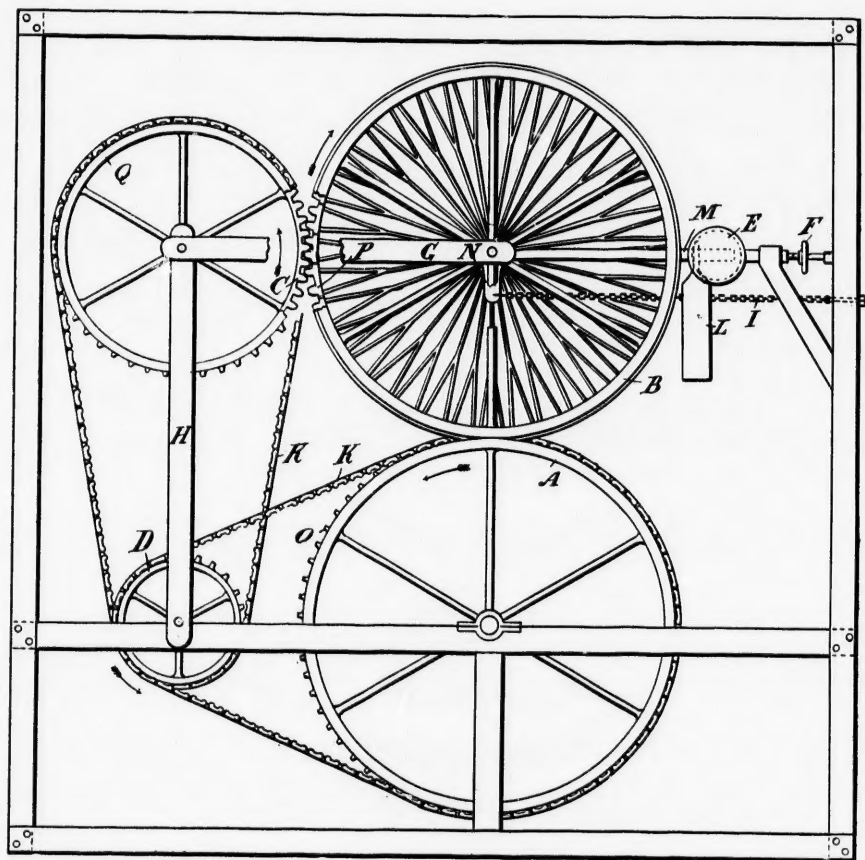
Élévation, ou vue de front, du Moteur Centripète Horizontal.
